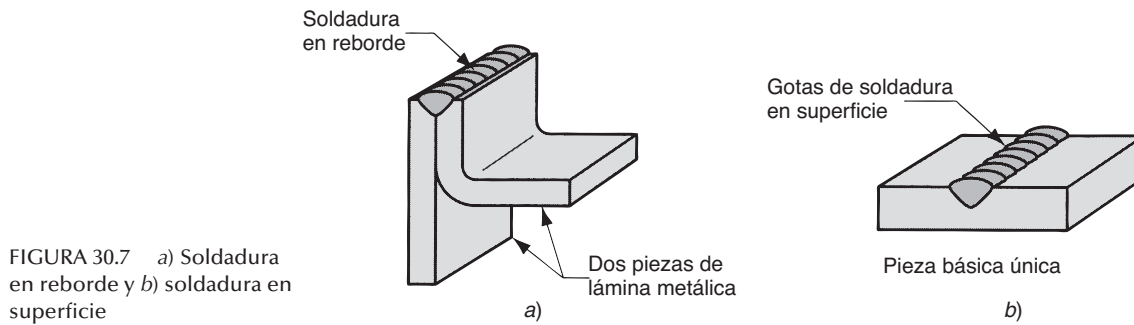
a) Soldadura en reborde y b) soldadura en superficie
